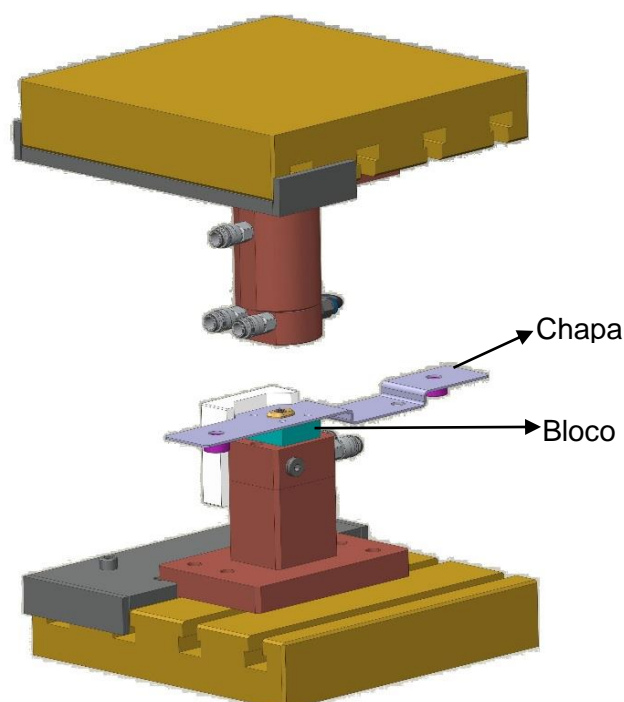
Esquema de montagem dos componentes na ferramenta de soldar.
